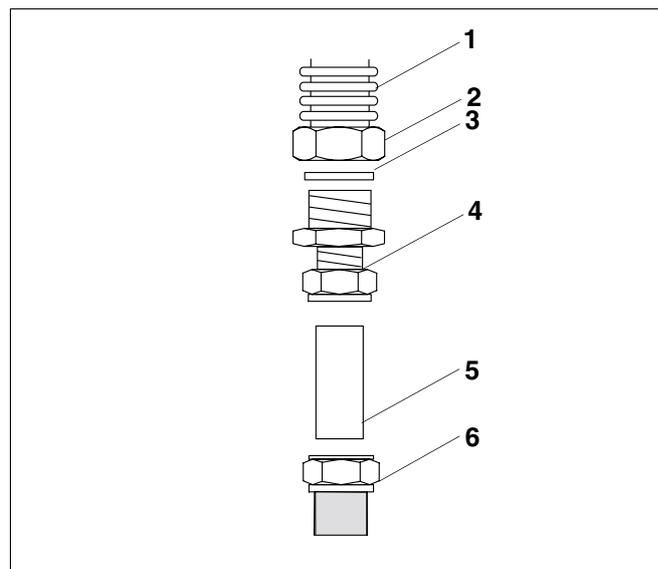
Raccordement Twin Tube DN 20 sur écrou-raccord avec bague de serrage de 22 mm
